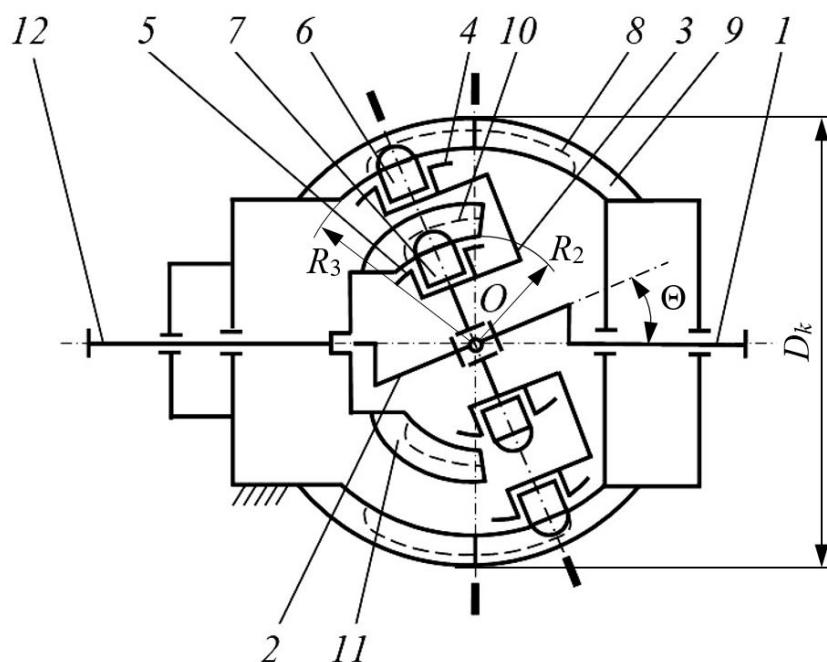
Кинематическая схема сферической роликовой передачи с двухрядным сателлитом
